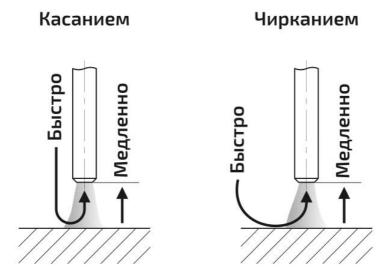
Способы зажигания сварочной дуги.
